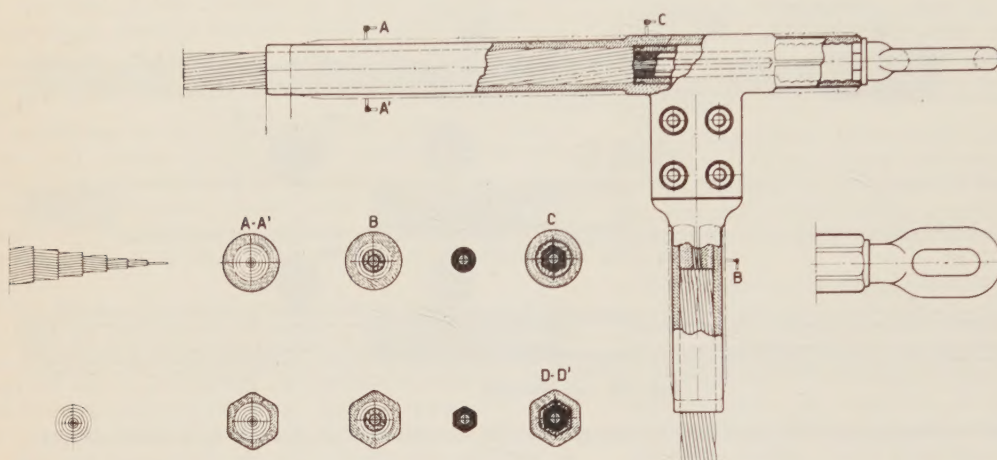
Morsa di ormeggio e giunto a compressione per conduttore espanso, brevetto Alcoa (costruzione SALVI).
